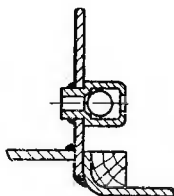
Дефекты конструкции предохранительного клапана цилиндра ВМГ.
